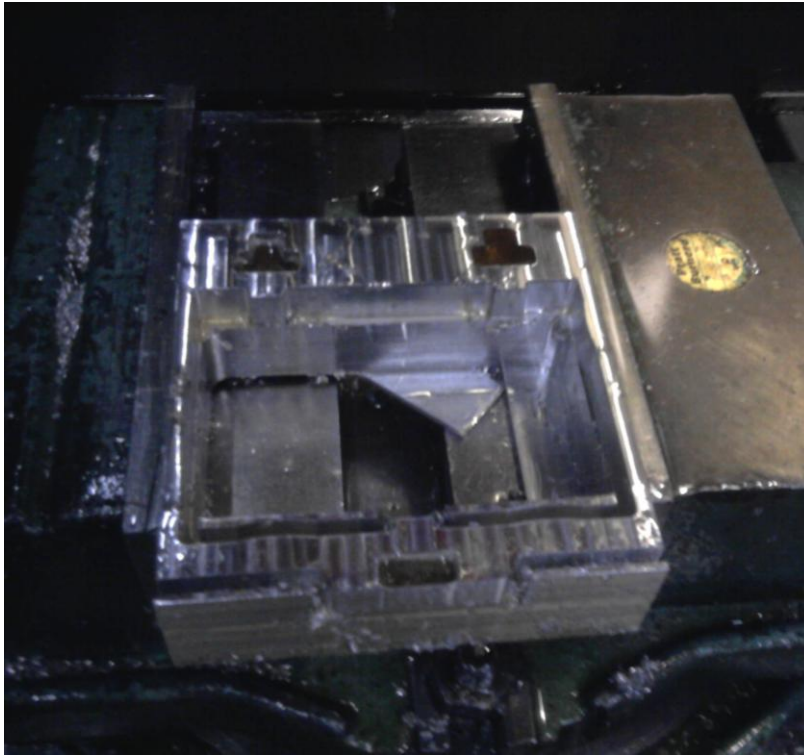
Bloque de material fijo en la máquina CNC.
